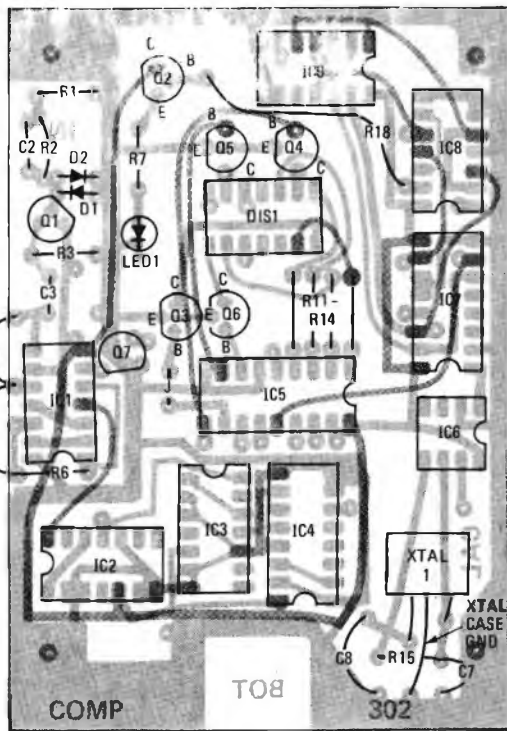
Posizione ed orientamento della maggior parte dei componenti presenti su un lato della piastrina di supporto.
